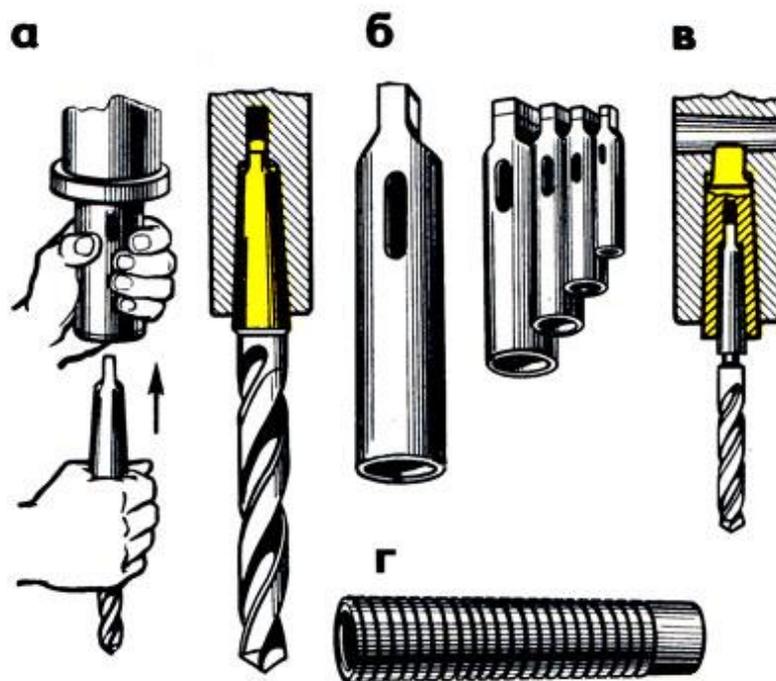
Крепление инструмента: а - непосредственно в шпинделе станка, б - переходные конические втулки, в - при помощи переходной втулки; г - переходная втулка из пружинной проволоки
